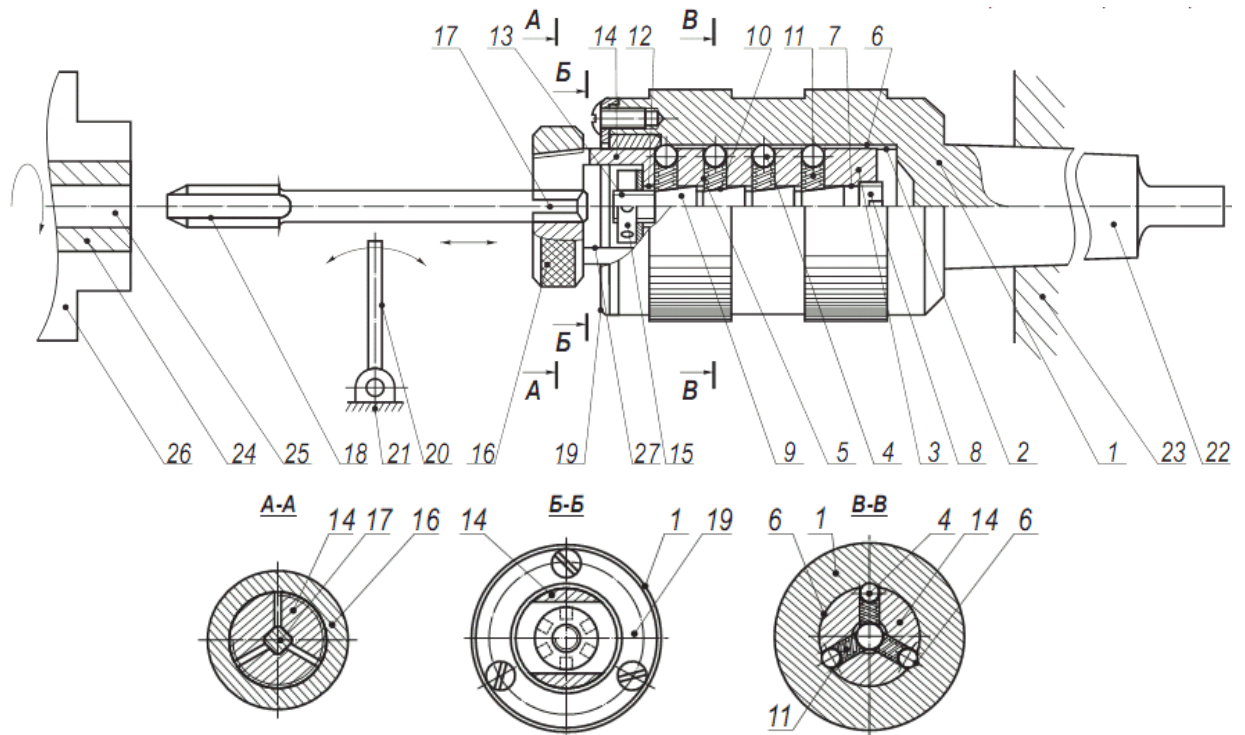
Запобіжний патрон для осьових інструментів [21]
